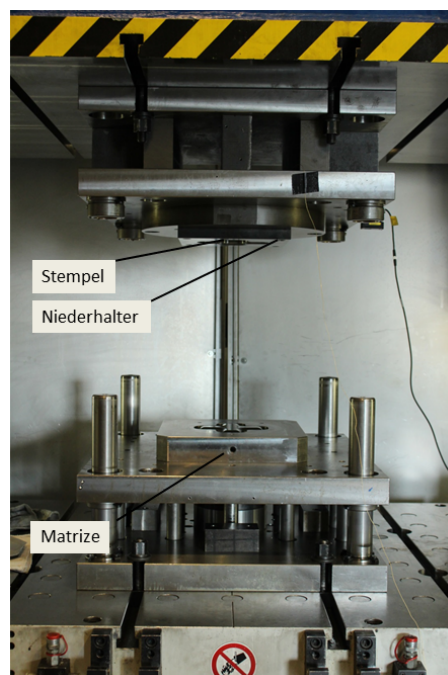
Eingebautes Werkzeug in der hydraulischer Presse der Firma Schuler
